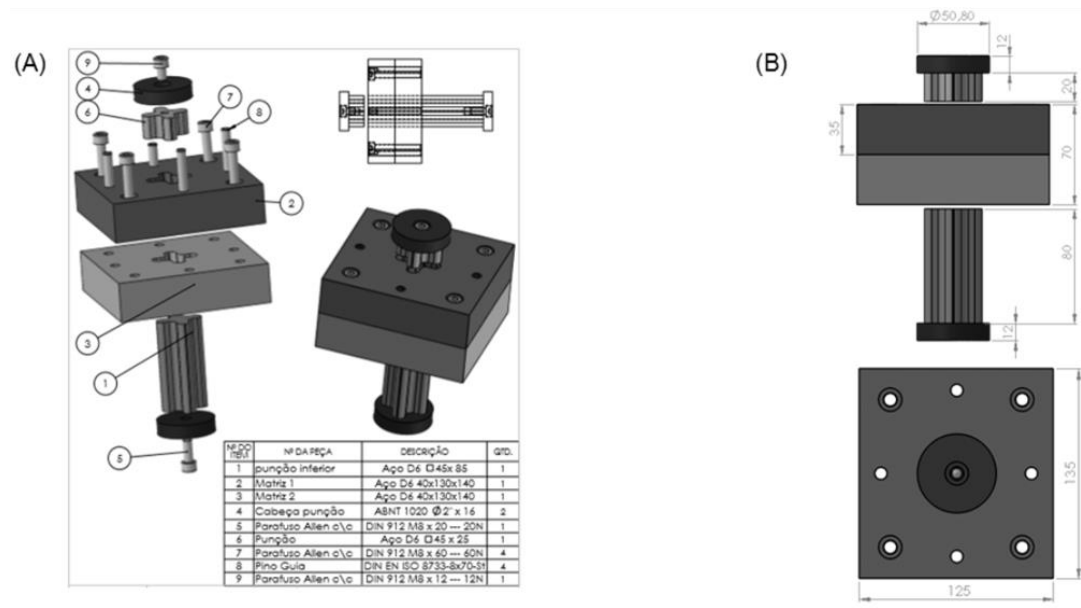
Perspectiva e vista explodida (A) e dimensões externas do ferramental (B)
